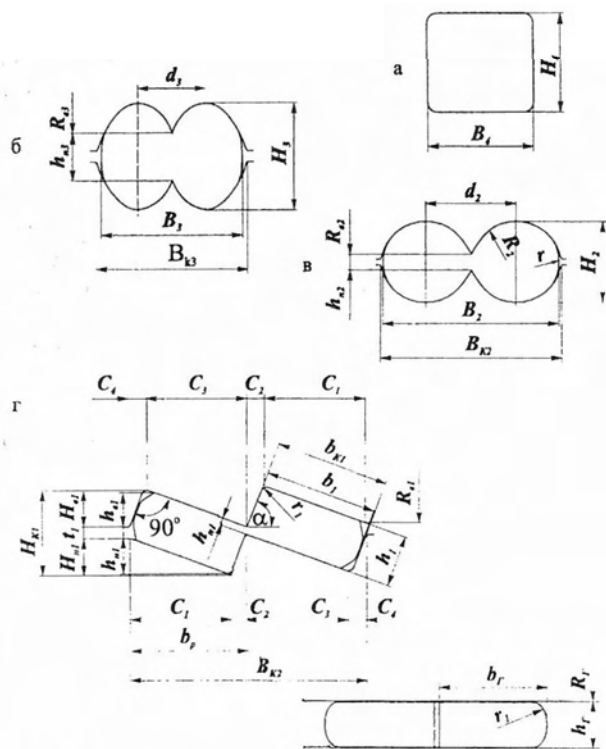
Схема калибровки валков для двухручьевой прокатки-разделения сортовых профилей с продольным разделением раската прокаткой в гладких цилиндрических валках; а + г - очередность расположения калибров.
